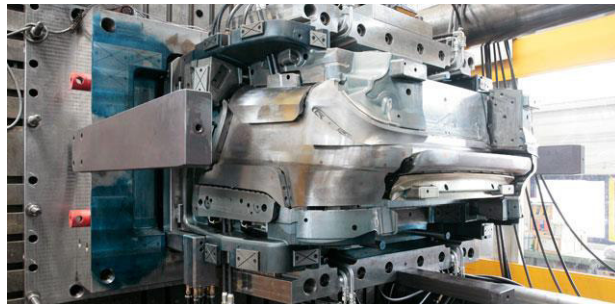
Spritzgießwerkzeughälfte für eine Frontstoßstange
